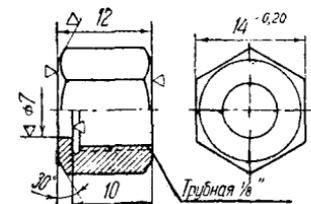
Дет. № 100-03. Гайка соединительная масляной трубки контроллера
